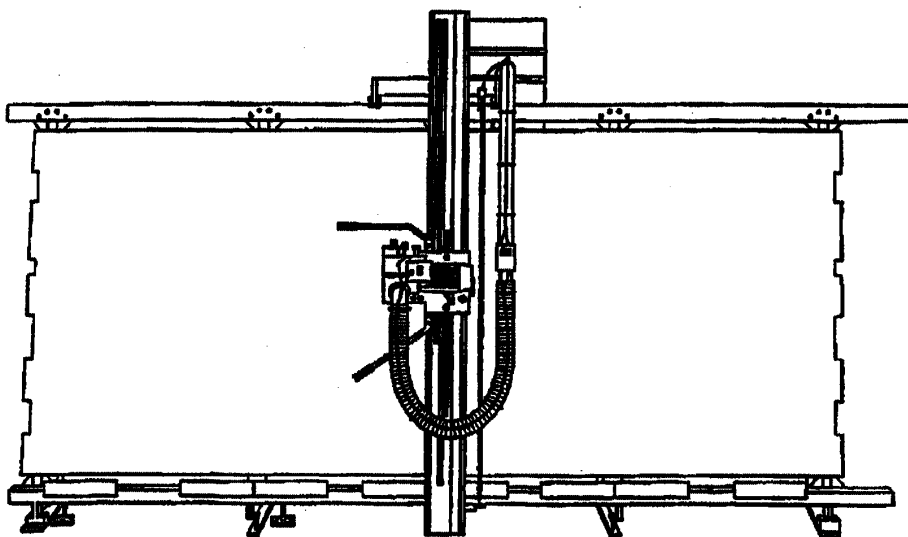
а – Пример круглопильного вертикального станка, у которого режущая часть дисковой пилы находится перед обрабатываемым изделием
